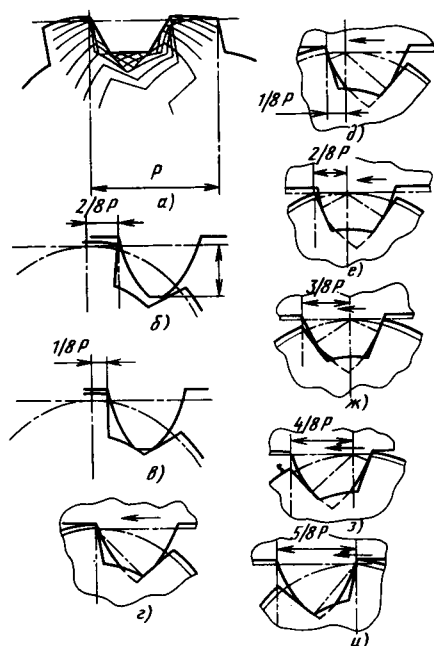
Схема работы фрезы постоянной установки с удлиненным зубом
